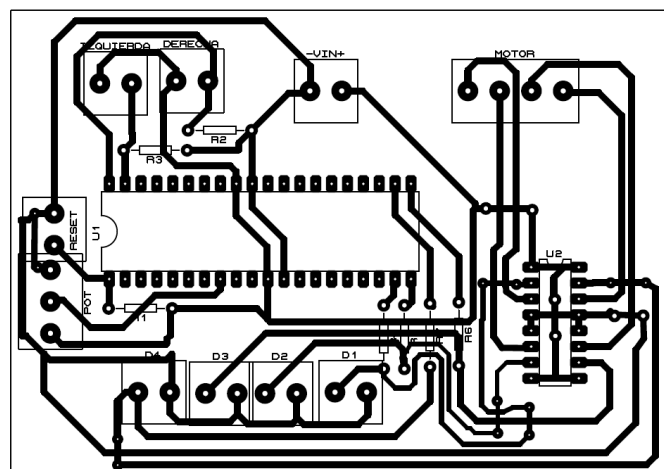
19: Tarjeta de circuito impreso de motor paso a paso bipolar
